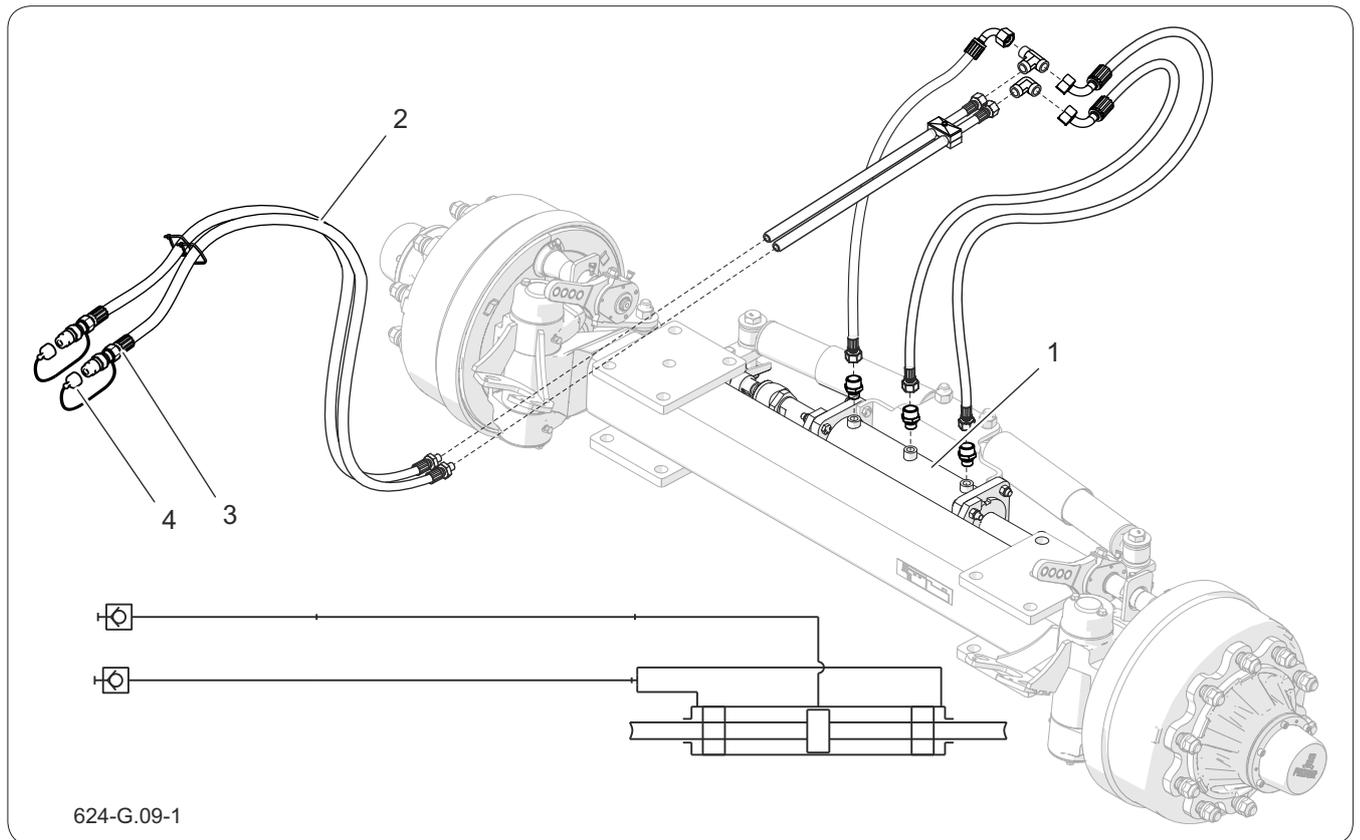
Aufbau und Schema der Installation des hydraulischen Lenkschlusses
